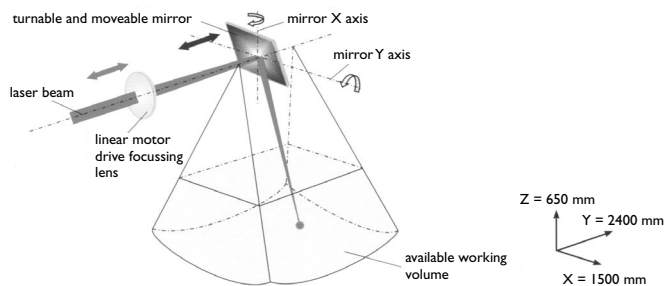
a. Remote welding system från Rofin Sinar.
